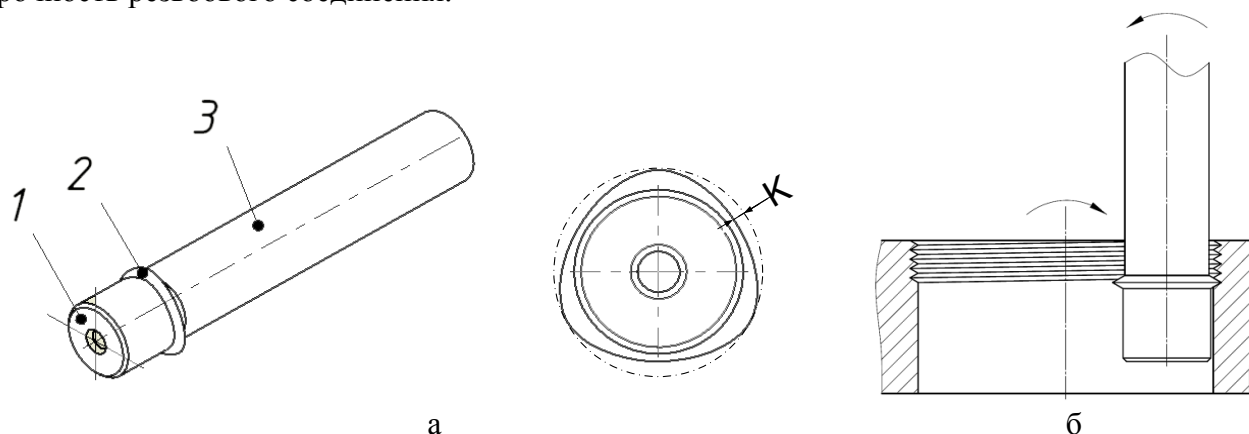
Конструкция предлагаемого инструмента (а) и вариант кинематической схемы обработки резьбы в готовом отверстии (б).
